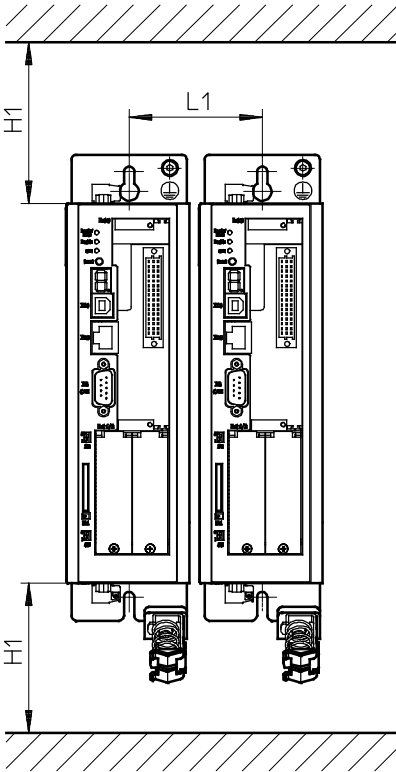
Motorcontroller CMMP-AS-...-M3: Montageabstand und Einbaufreiraum
